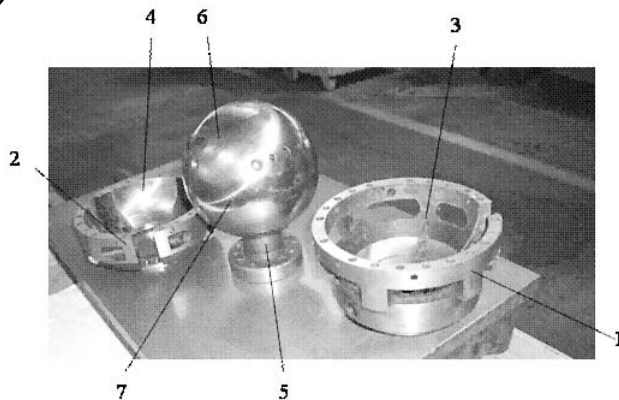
Основні деталі виготовленого опорного вузла та ділянки точних сферичних поверхонь деталей
